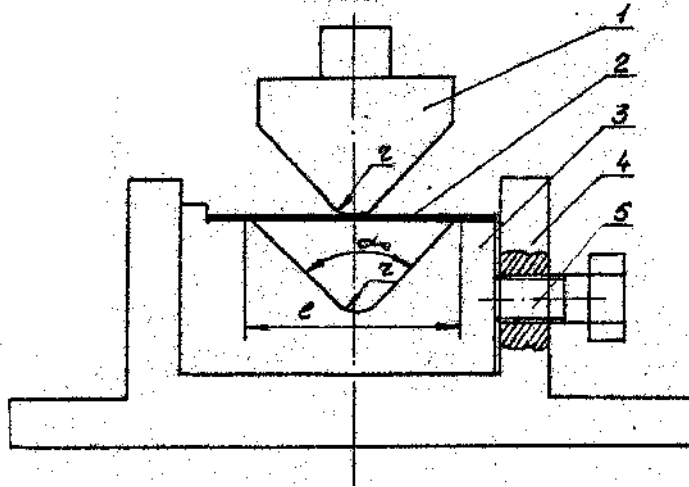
Схема штампа для гибки: 1 – пуансон; 2 – заготовка; 3 – матрица; 4 – корпус; 5 – стопорный винт.
